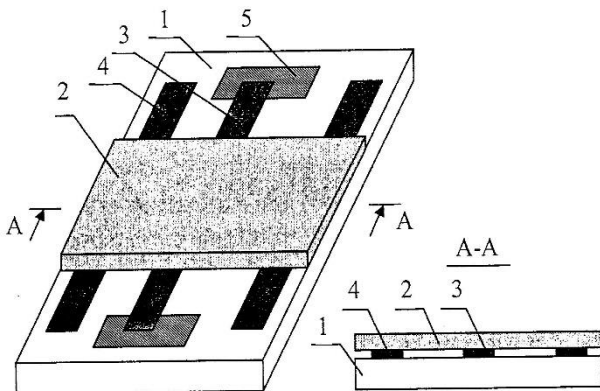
Товстоплівковий сенсор сили з „поясковим” опором: 1 - базова підкладка; 2 - верхня підкладка; 3 - п'єзочутливий резистор; 4 - опорний резистор; 5 - контактна площадка
